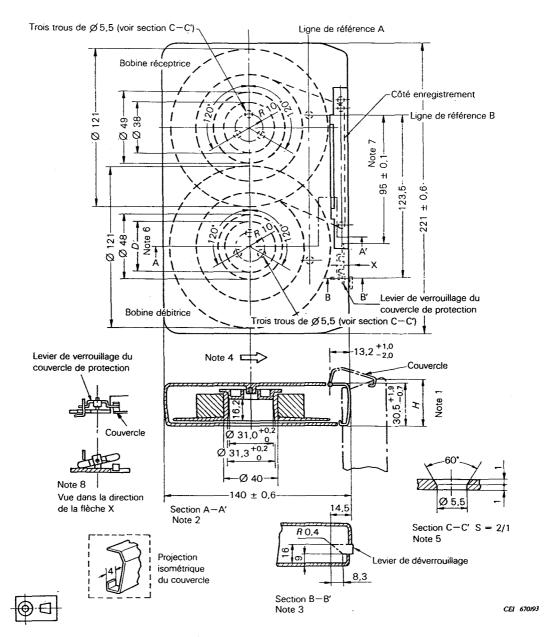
Emplacement des bobines et du couvercle de protection de la cassette
